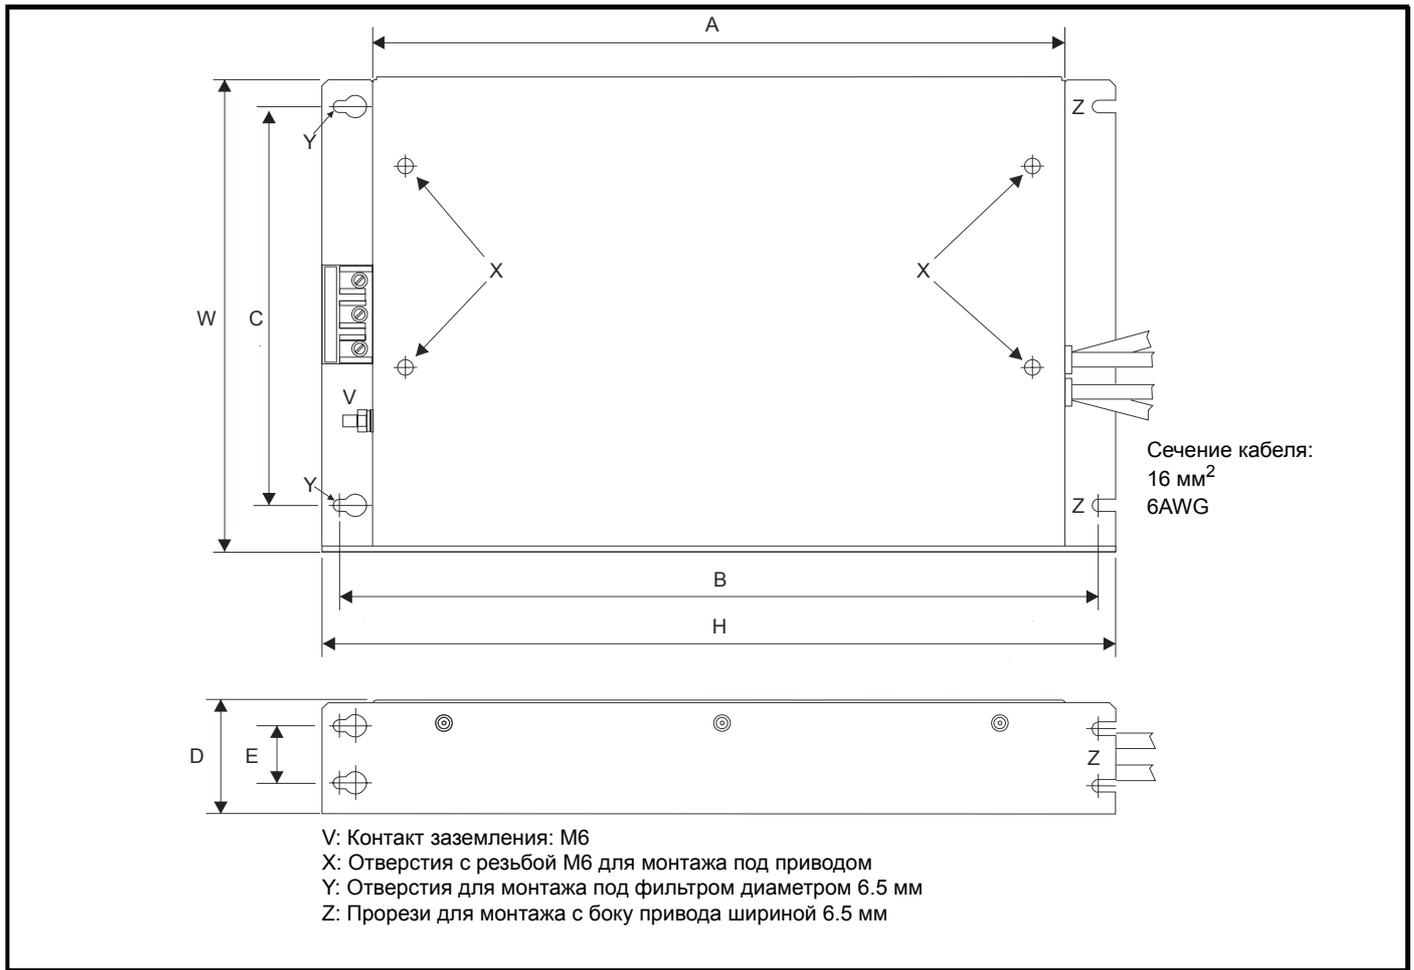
Внешний фильтр ЭМС габарита 2
